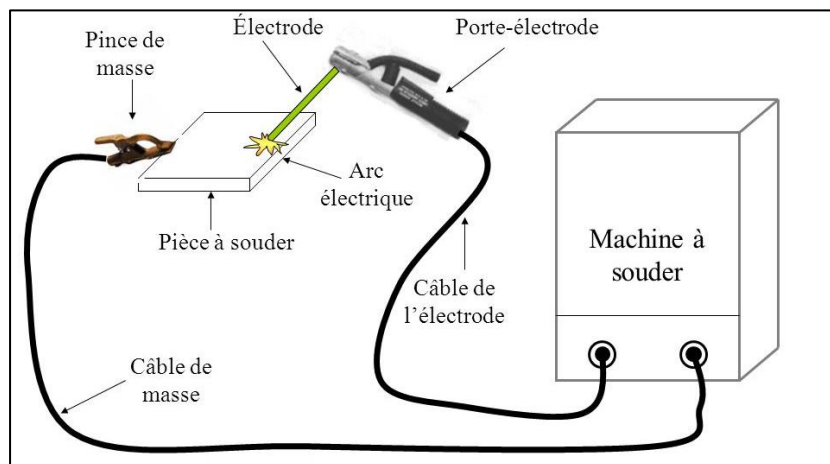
Circuit électrique pour le soudage à l'arc
